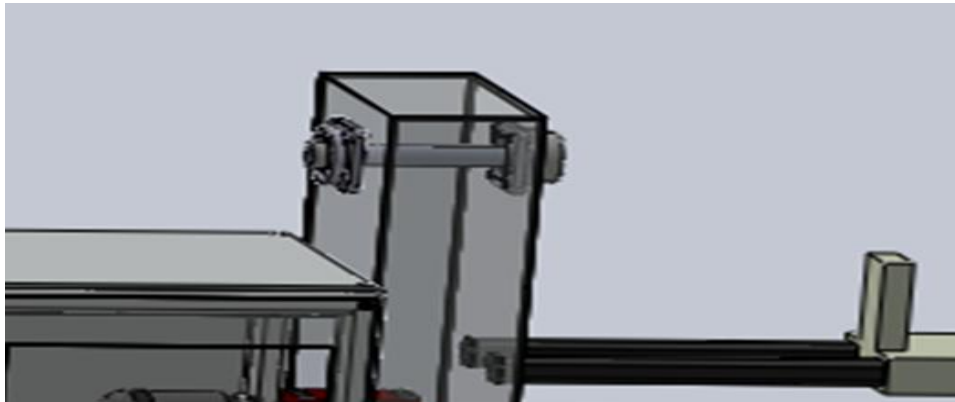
cabezal y eje de torsión diseñado en Solidworks. Fuente: Autor
